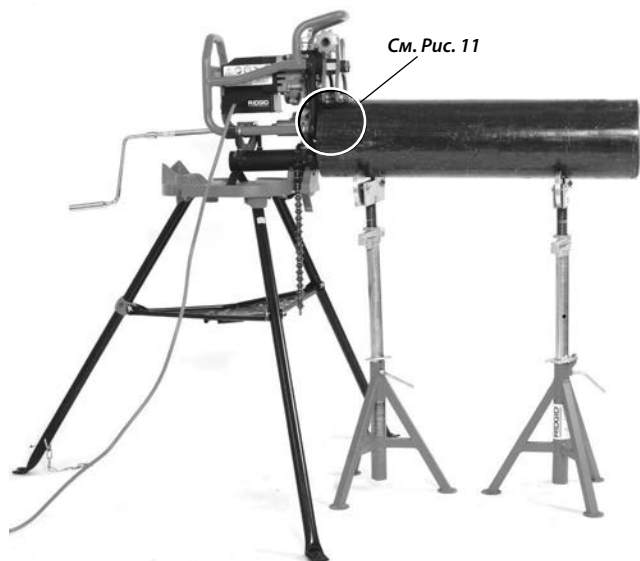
Закрепленный станок для снятия фаски, длинная труба, несколько опор для трубы
